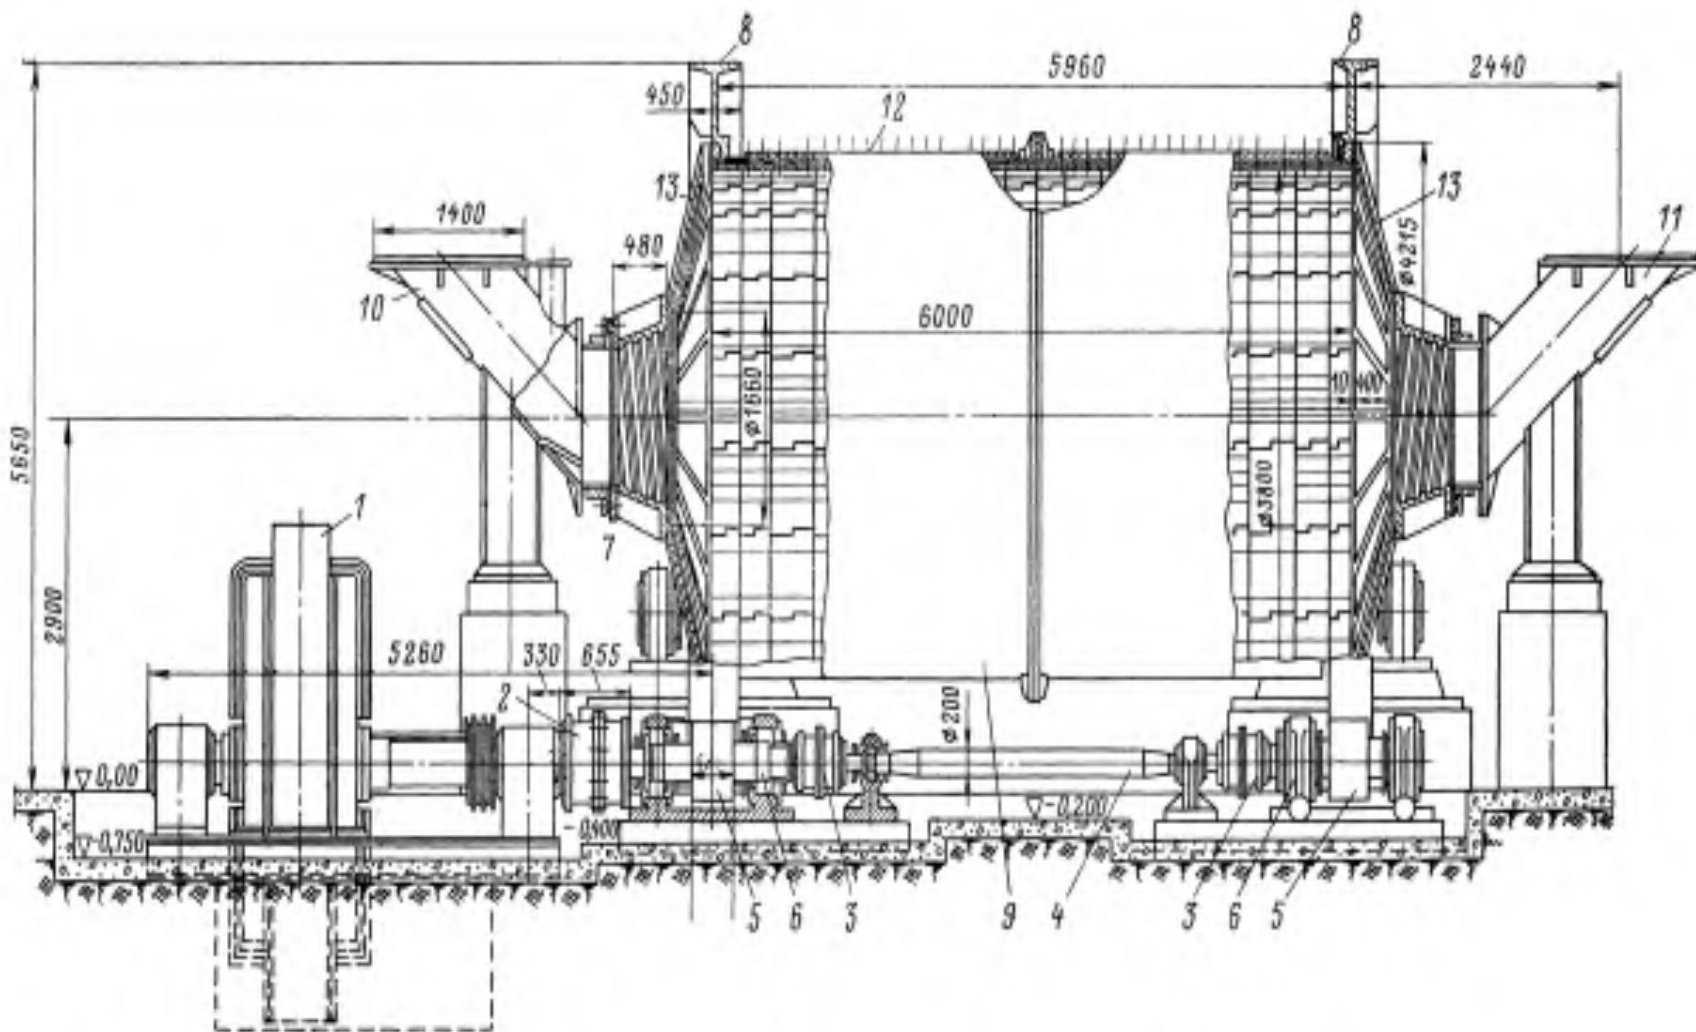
Шаровая барабанная мельница (ШБМ): 1 – электродвигатель; 2, 3 – зубчатые муфты; 4 – соединительный вал; 5 – приводные ролики; 6 – опорные подшипники качения; 7 – опорные ролики; 8 – гладкие цилиндрические венцы; 9 – барабан мельницы; 10 – углеподающий патрубок; 11 – пылевыдающий патрубок; 12 – цилиндрическая часть барабана; 13 – торцевые стенки
